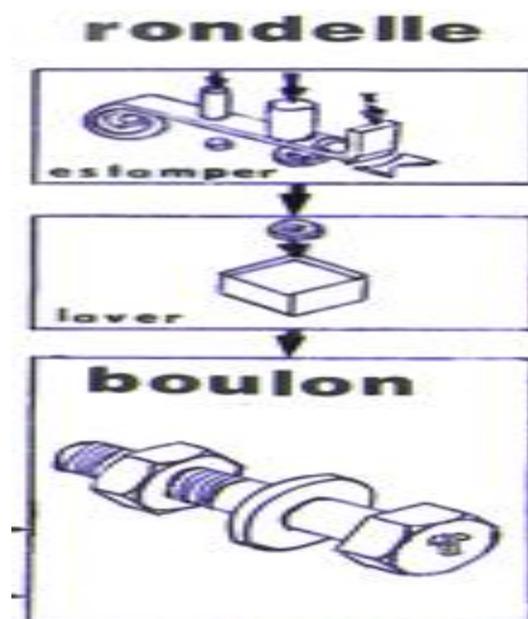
Les stations de machine d'usinage des rondelles. [22]
